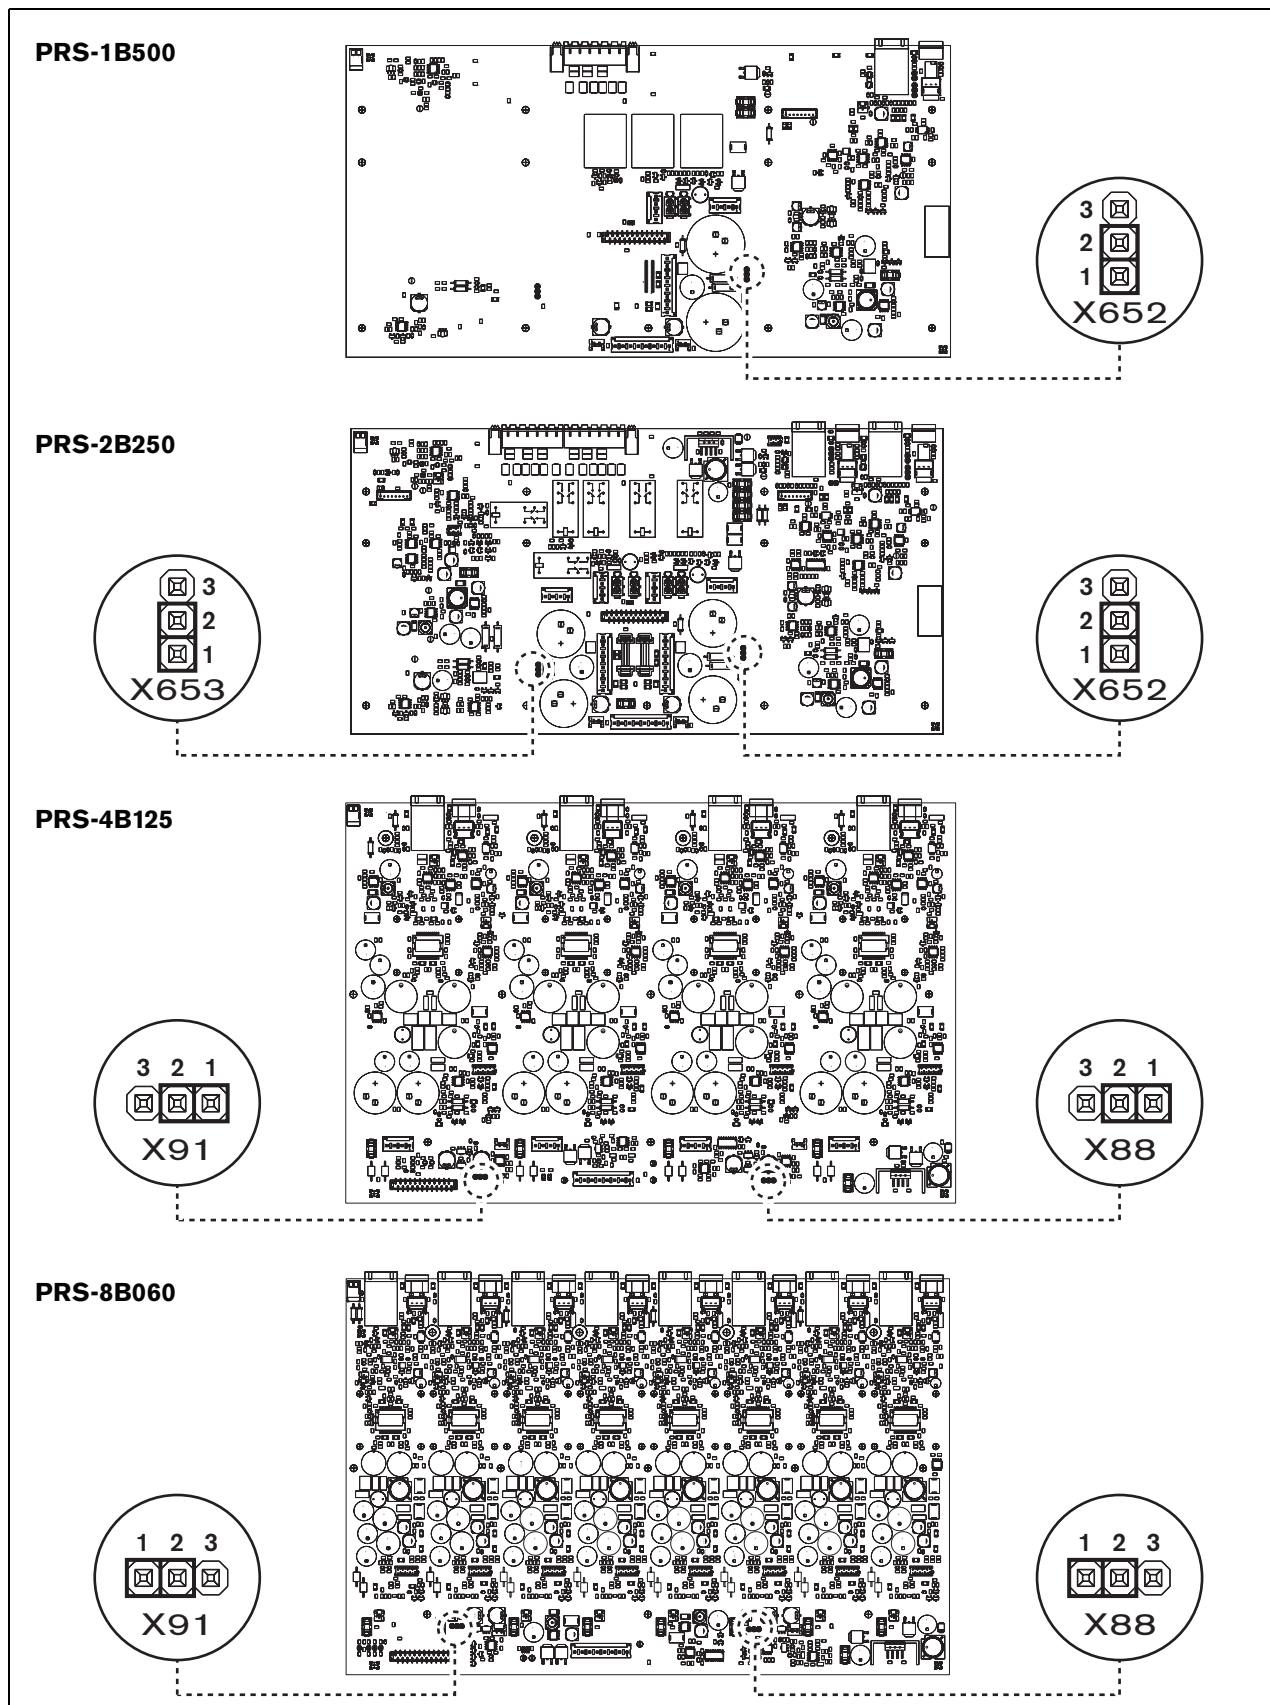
Draufsicht auf Ausgangsplatinen für Jumper mit Lüftersteuerung
